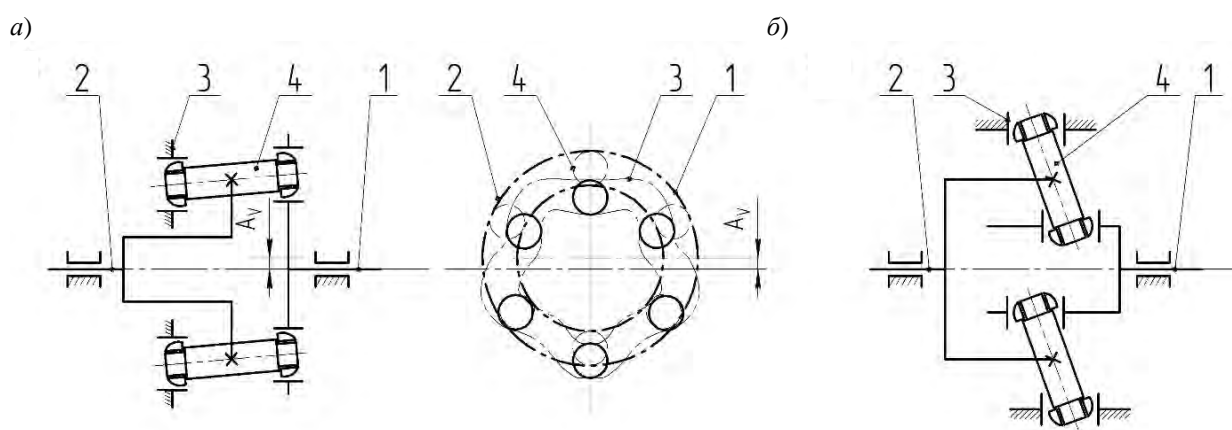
Кинематическая схема передачи с фиксированным расположением промежуточных тел качения: *а* – беговые дорожки расположены на плоских поверхностях (радиальный тип передачи); *б* – беговые дорожки расположены на цилиндрических поверхностях (цилиндрический тип передачи)
